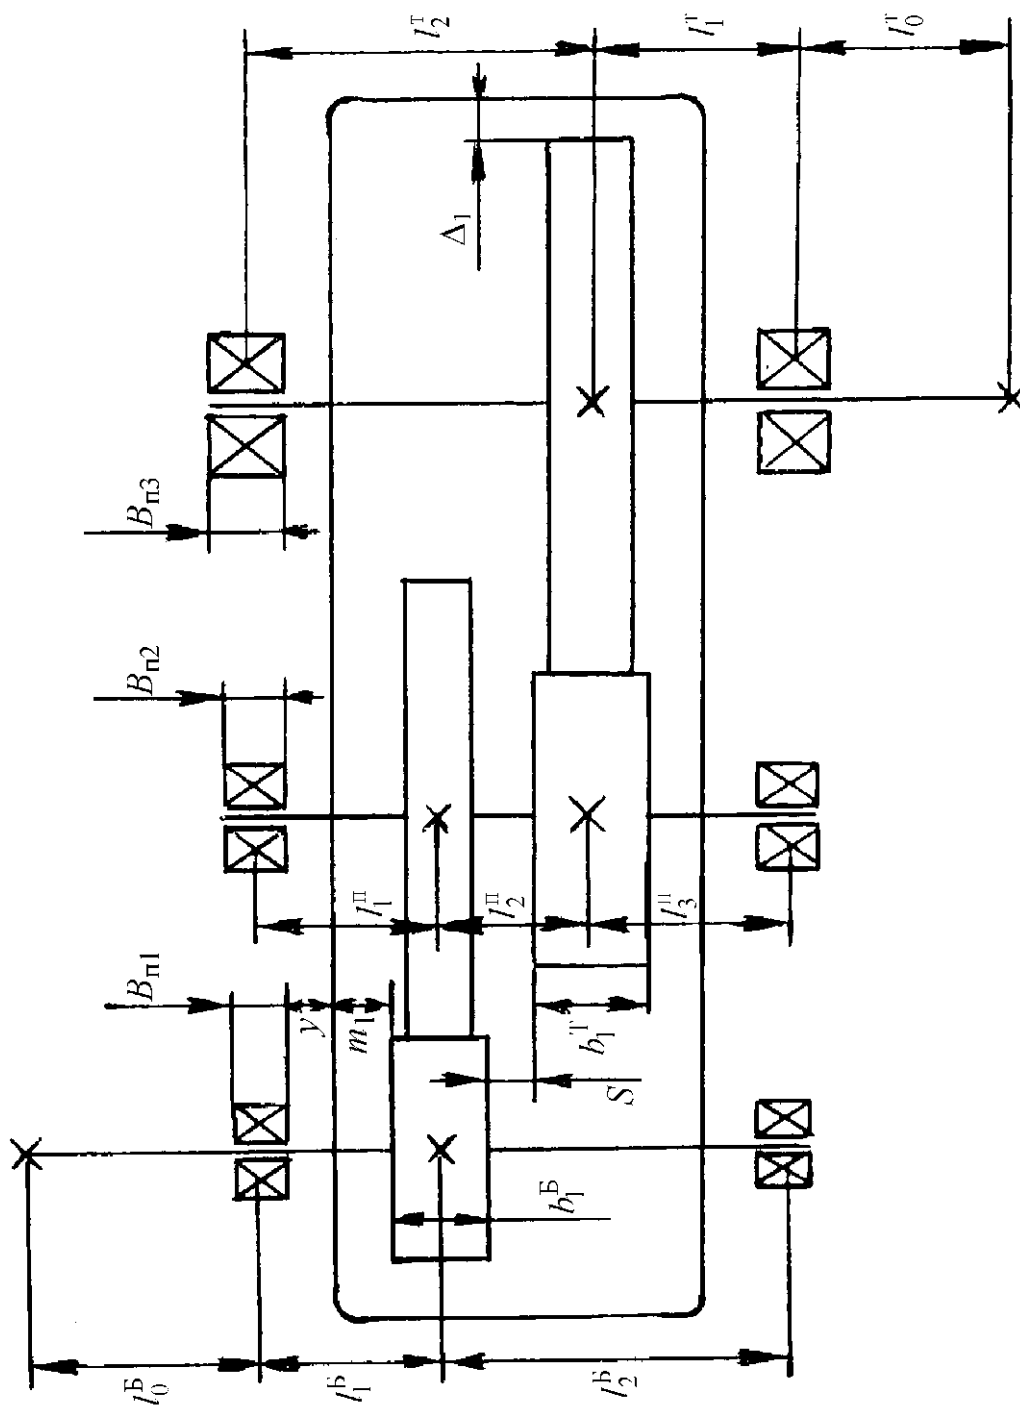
Эскизная компоновка двухступенчатого цилиндрического редуктора
